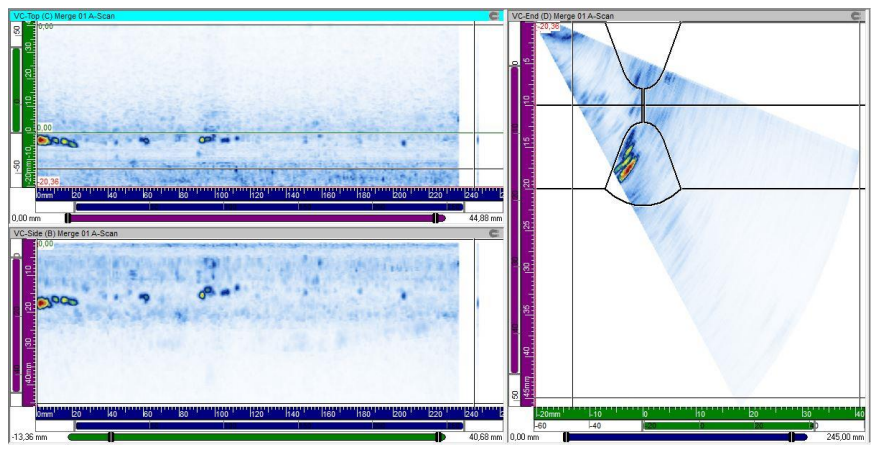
Výsledek měření vzorku č. 3 ze strany A před korozním testem
